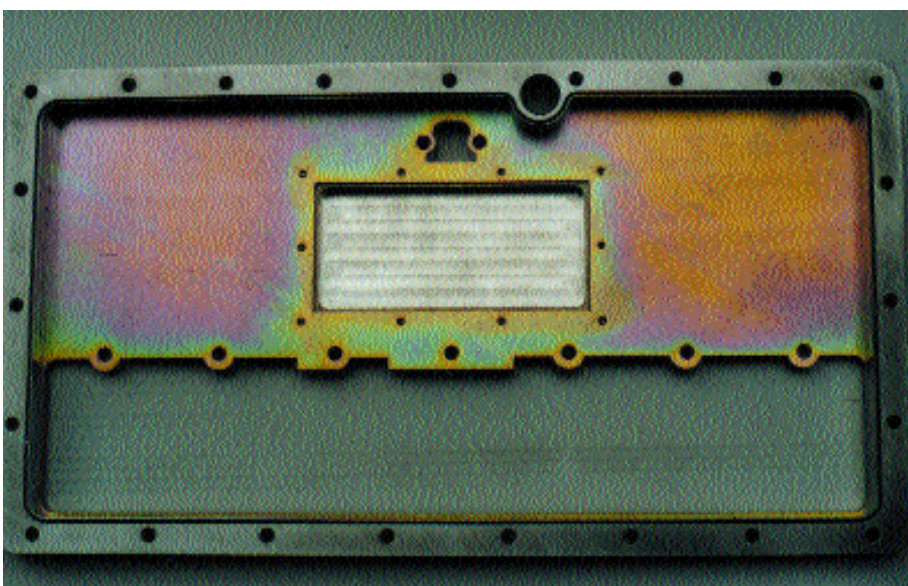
Alurahmen mit O-Ring auf Trägerblech
